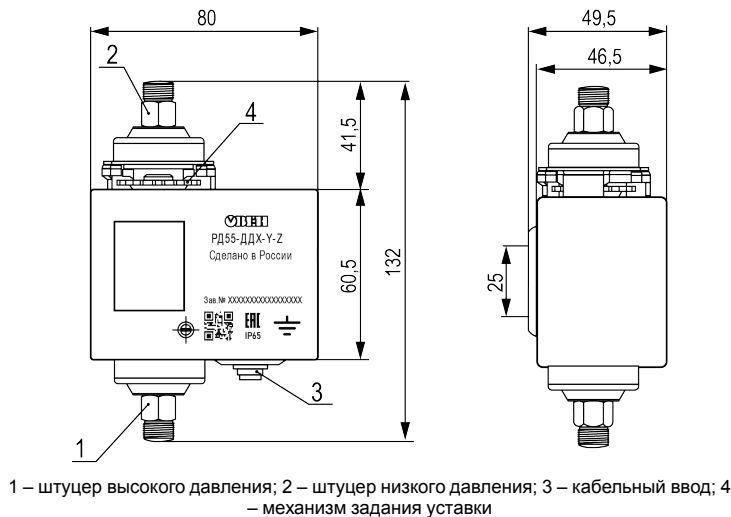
Габаритные и присоединительные размеры прибора
